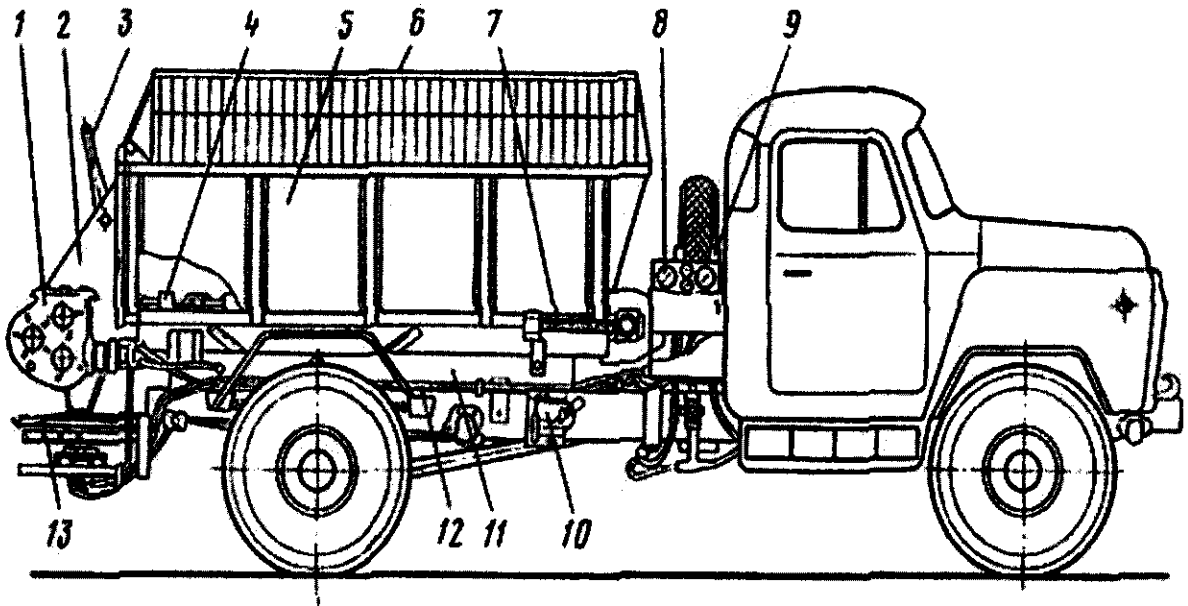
Разбрасыватель универсальный КО-104А (1 - редуктор привода конвейера 2 - бункер; 3 - рычаг шибера, 4 - скребковый конвейер, 5 - кузов. 6 – решетка, 7 – механизм натяжения конвейера, 8 - пульт управления, 9 – кронштейн запасного колеса, 10 - насос; 11 – надрамник, 12 - гидросистема; 13- разбрасывающий диск)
